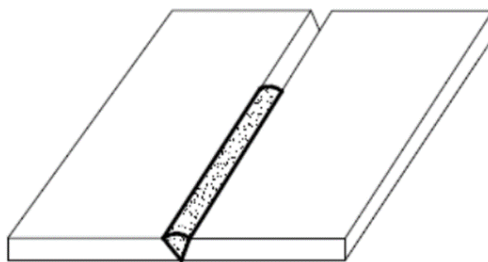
Soldadura plana. Fuente: Rodríguez (2016).
